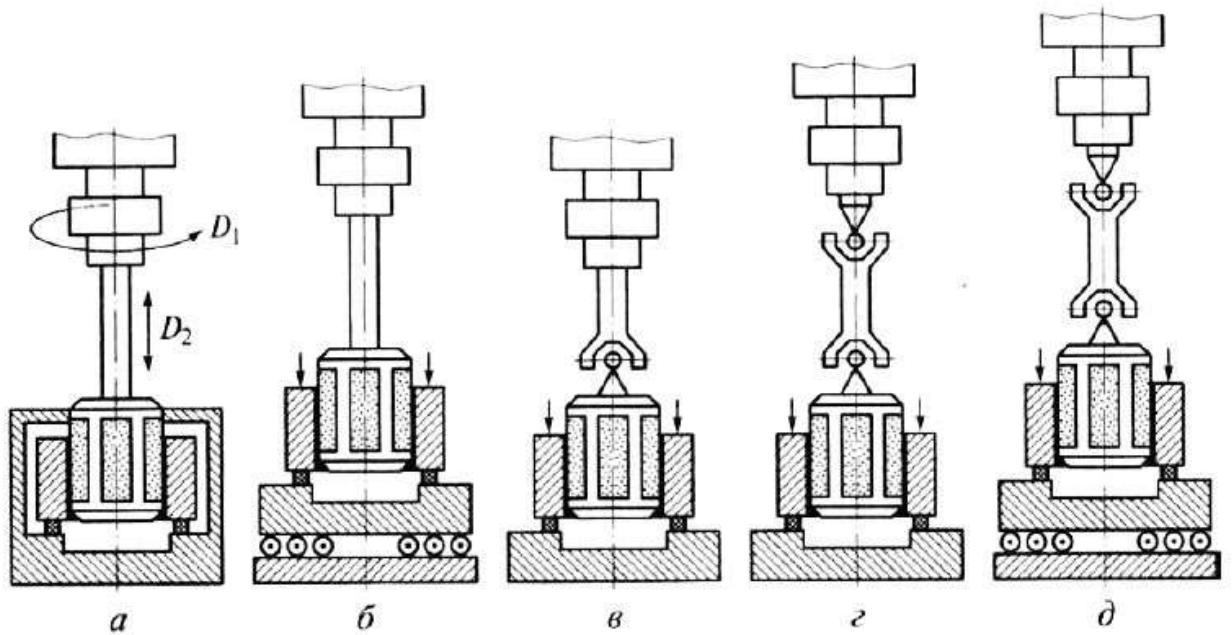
Схема кріплення хона за різної кількості ступенів свободи заготовки: а – жорстке при двох ступенях свободи заготовки; б - жорстке при чотирьох ступенях свободи заготовки; в – одношарнірний при двох ступенях свободи заготовки; г - двошарнірне при двох ступенях свободи заготовки; д - двошарнірне при чотирьох ступенях свободи заготовки.
